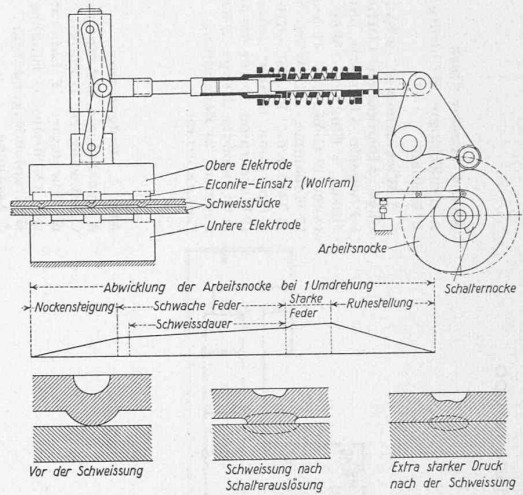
Schema der Arbeitsweise einer Buckel-Schweissmaschine
